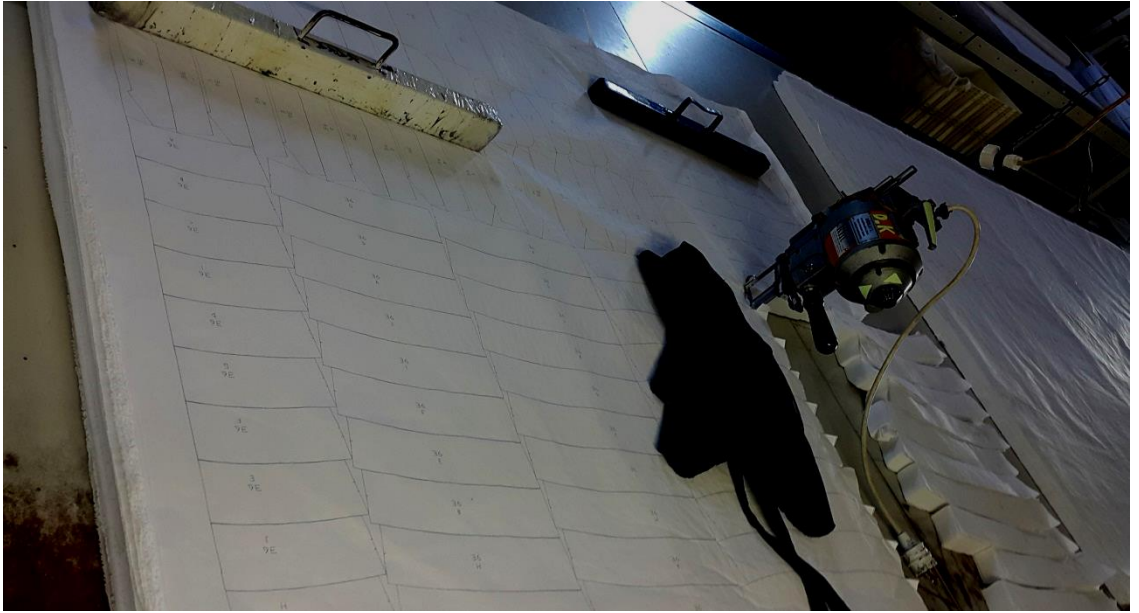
Kumaş Pastal Planı (Rembrandt)
